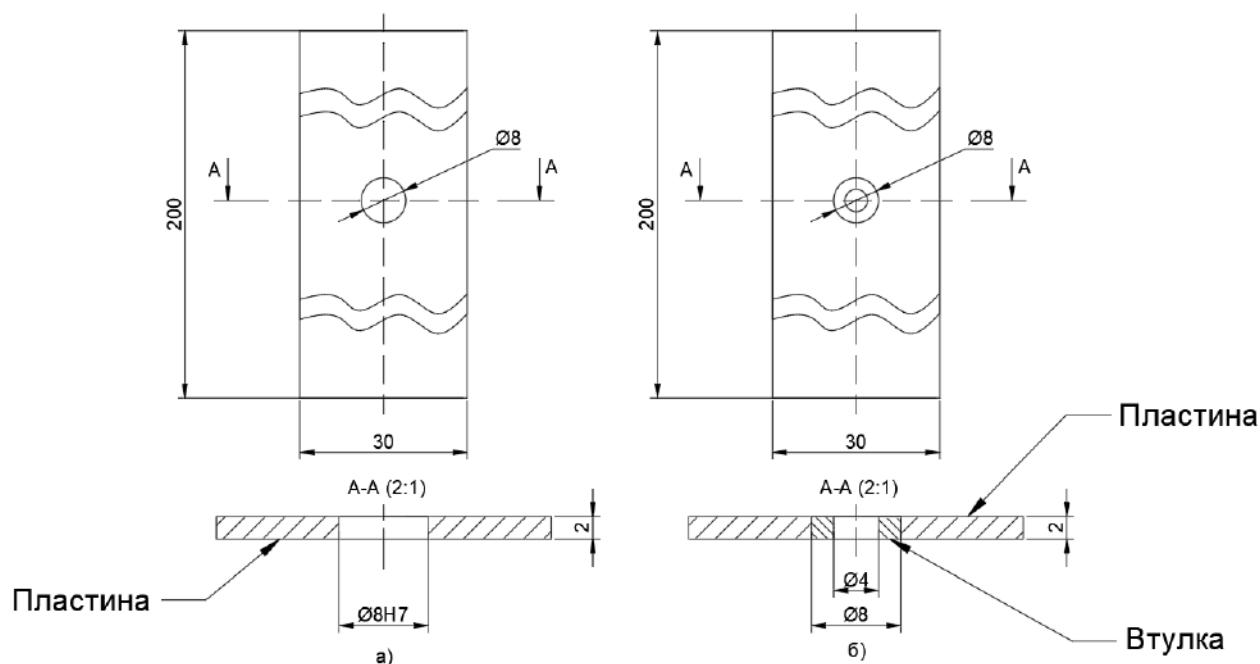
Геометрия опытных образцов: а) – образец со свободным отверстием; б) – образец с установленной втулкой
